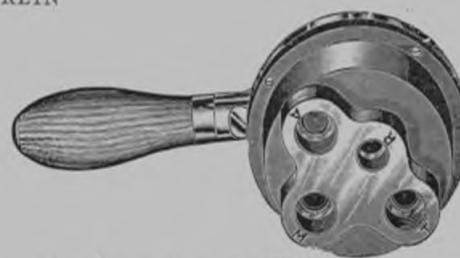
ROBINET DE MANŒUVRE (VUE EN DESSOUS)
